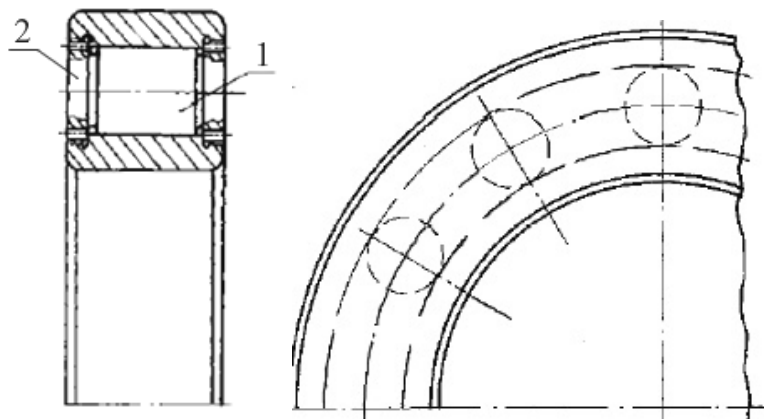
Бессепараторный роликовый подшипник качения (RU 2135851, Н.В Филонов, В.Л. Юрьева, Г.А. Матвеев)
